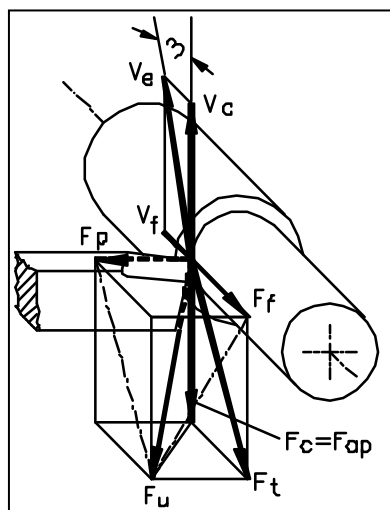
Força de usinagem e suas componentes no processo de torneamento (FERRARESI, 1977)
